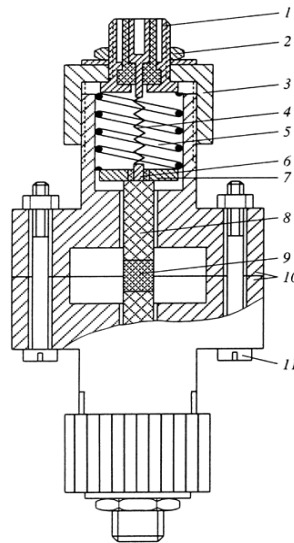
Конструкция акустического устройства: 1 - разъем стандартного типа (СРГ-50-273); 2 - гайка  $\varnothing 0.15$ ; 3 - гайка  $\varnothing 1.2$ ; 4 - пружина; 5 - пружина; 6, 7 - электрод; 8 - нерезонансные пьезоэлементы цилиндрической или параллелепидной формы из ниобата лития  $x$  или  $z$ -срезов; 9 - исследуемый образец; 10 - конструкция акустического устройства; 11 - болты
